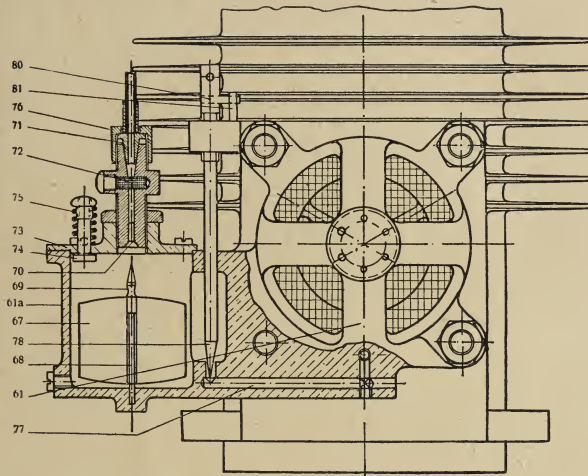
Grade-Vergaser. Querschnitt durch das Schwimmergehäuse
